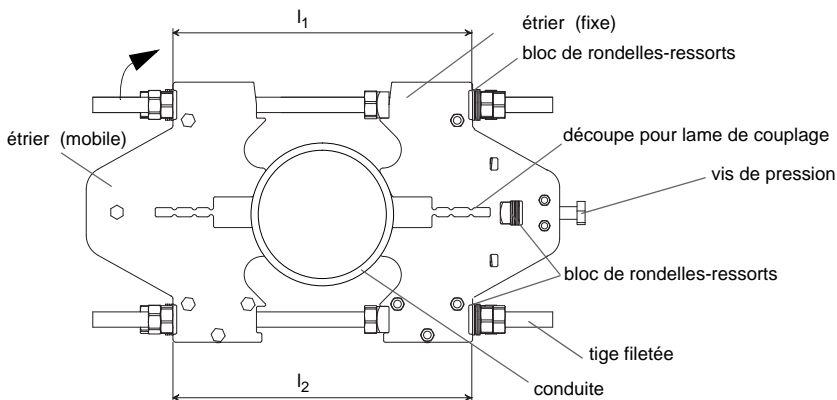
Le dispositif de fixation à la conduite sur la conduite (vue de l'avant)
